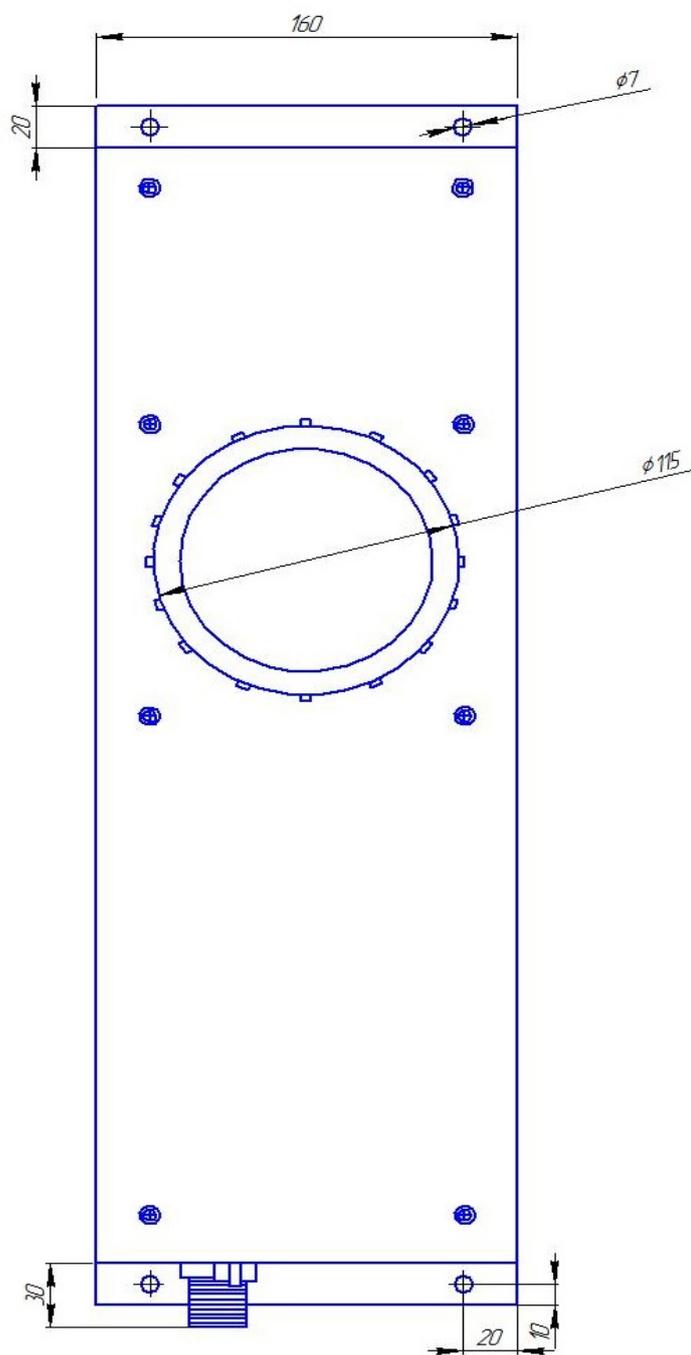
Габаритный чертёж ТКМWS-10-
